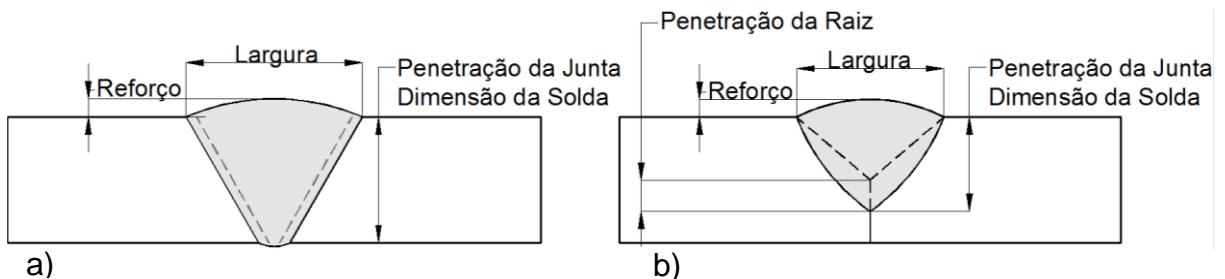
Dimensões da solda em junta V: a) penetração total da junta; b) penetração parcial da junta.
